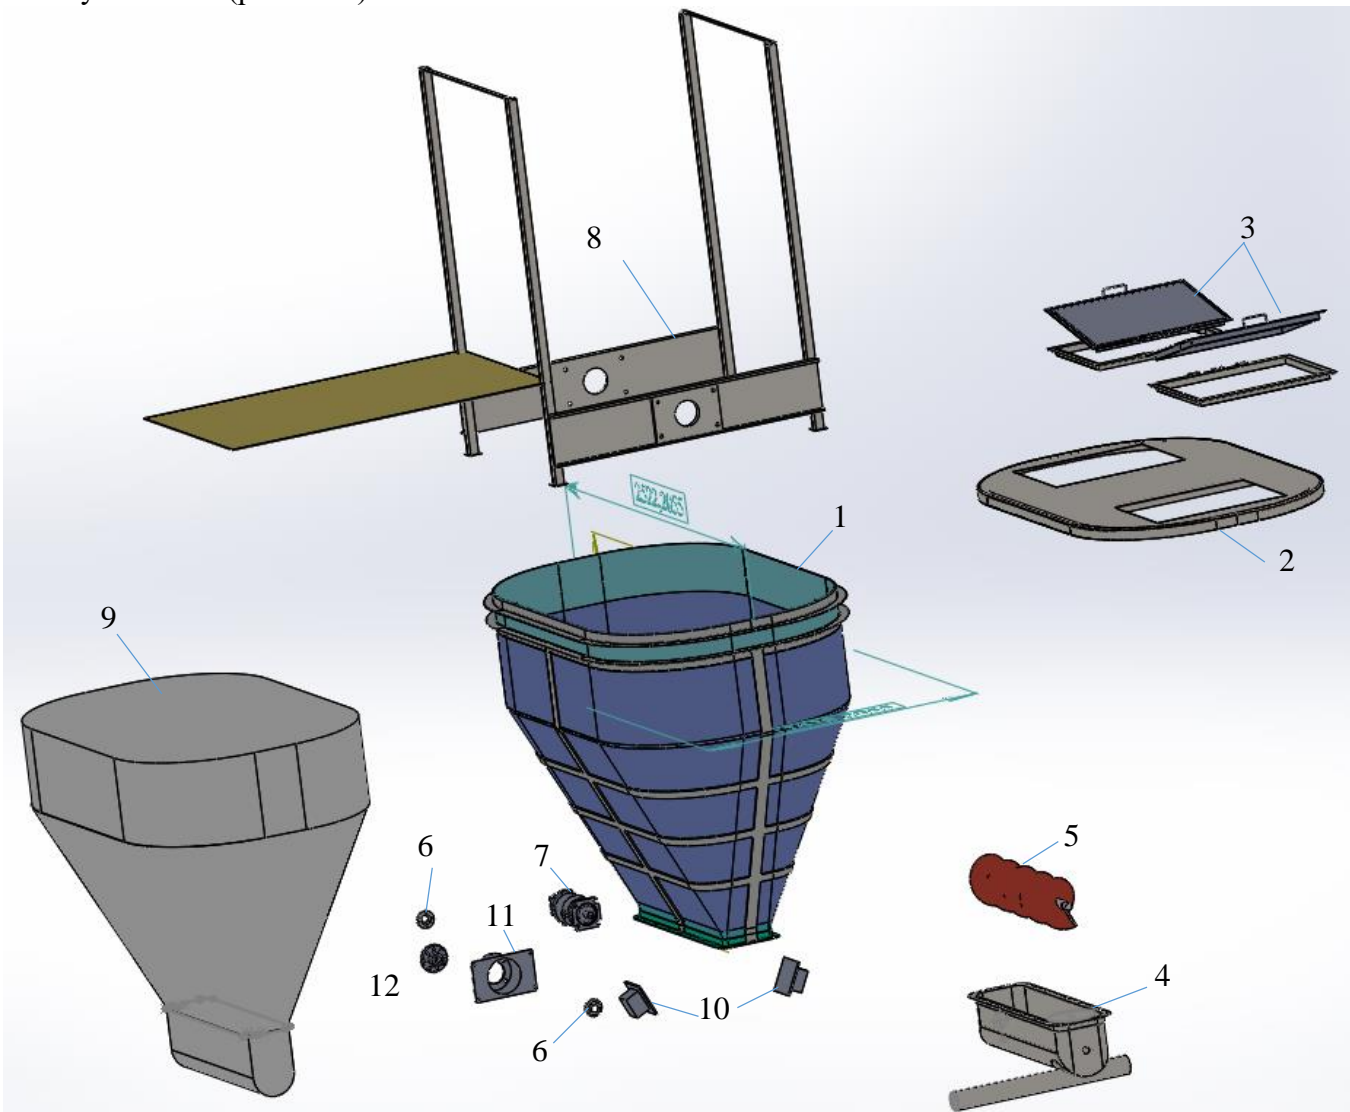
Эскизная модель бункерная системы насосной установки. Вид с разнесенными частями: 1 – корпус бункера; 2 крышка бункера; 3 – люк крышки; 4 – корпус шнека; 5 – шнек; 6 – опоры шнека; 7 – гидромотор; 8 – стойка бункера; 9 – тело цементного порошка. 10 – вибратор бункера; 11 – кронштейн двигателя; 12 – муфта
